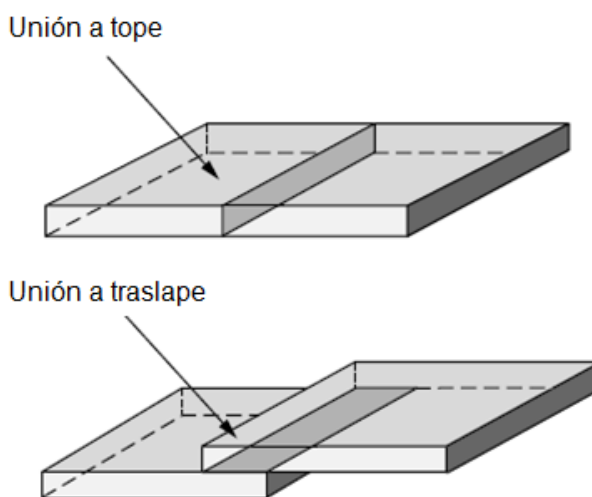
Tipos de diseño de unión básicos en soldadura: a tope y traslape. Figura extraída de la referencia (1)
